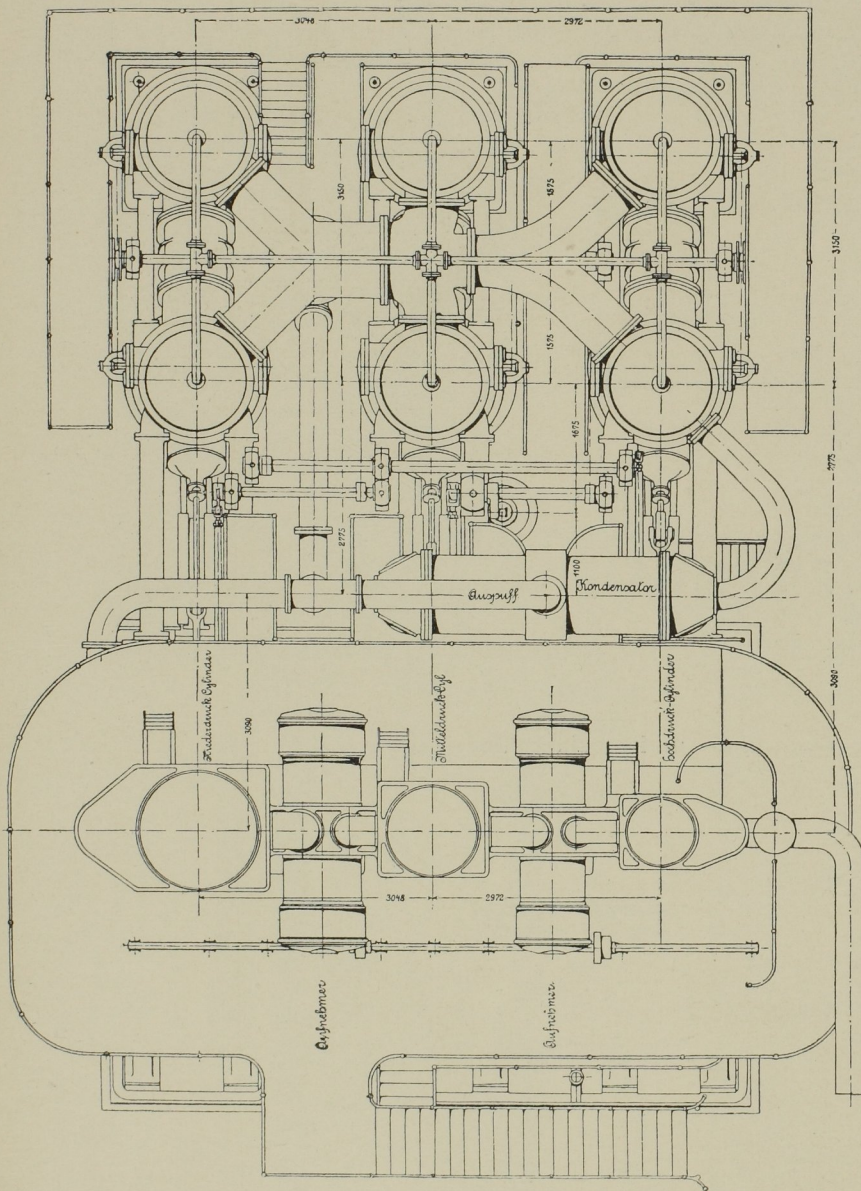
Grundriss der Pumpmaschine. Masst. 1:90.
